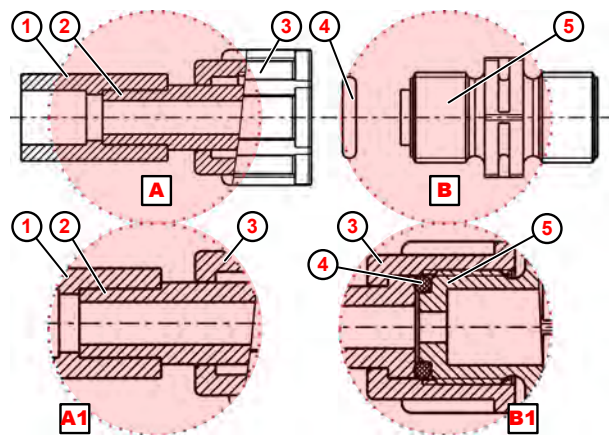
Rohranschluss mit Aufschweisssverbindung
